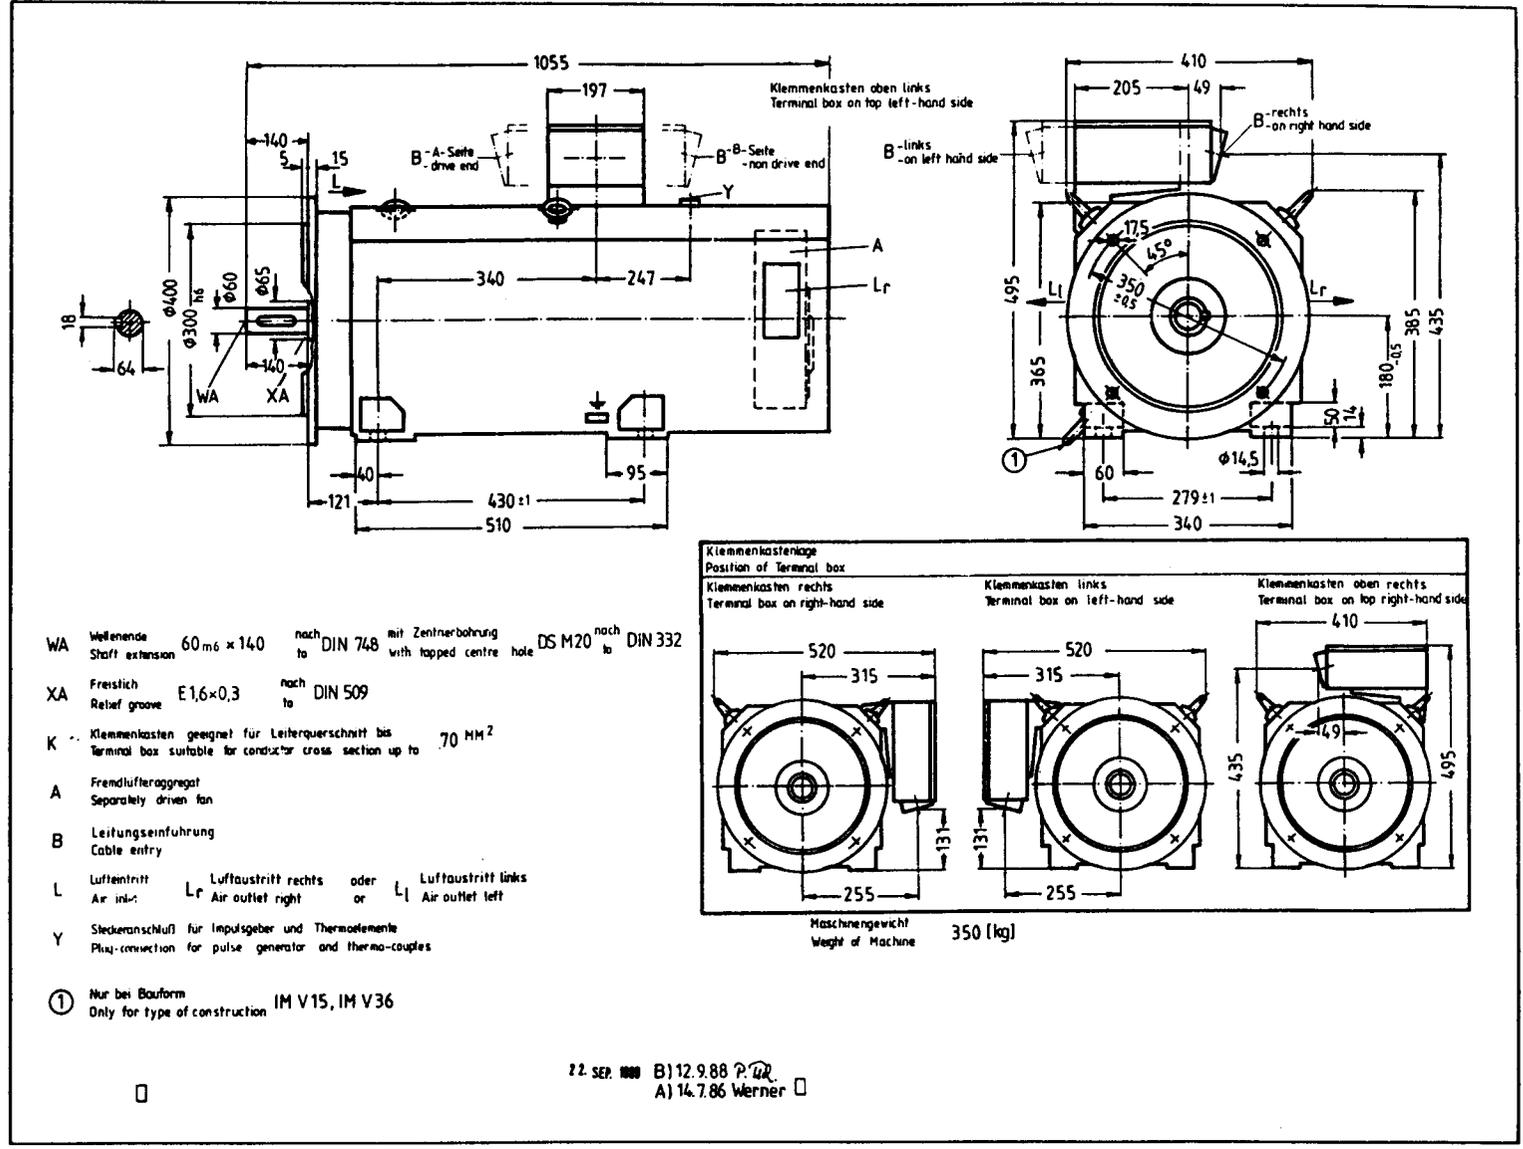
Maßblatt Drehstrommotor 1PH6 186-4C, Bauform IM B3 (Maße in mm, ohne Maßstab)
